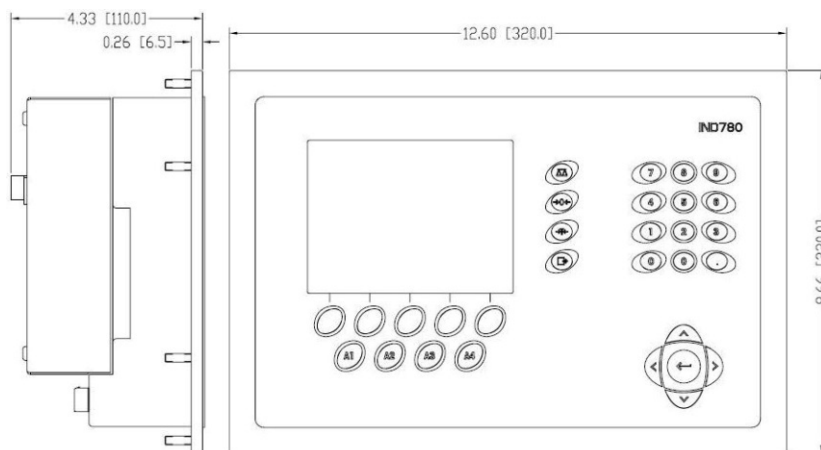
Dimensiones del terminal IND780batch para montaje en panel
